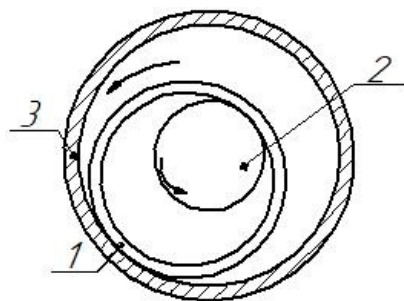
Почвообрабатывающий каток с фрикционно-планетарный вибровозбудителем с внутренней обкаткой: 1 – гладкий цилиндр; 2 – цилиндр; 3 – пустотельный цилиндр
